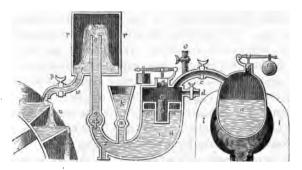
Machine et roue hydraulique de Papin, 1707.
